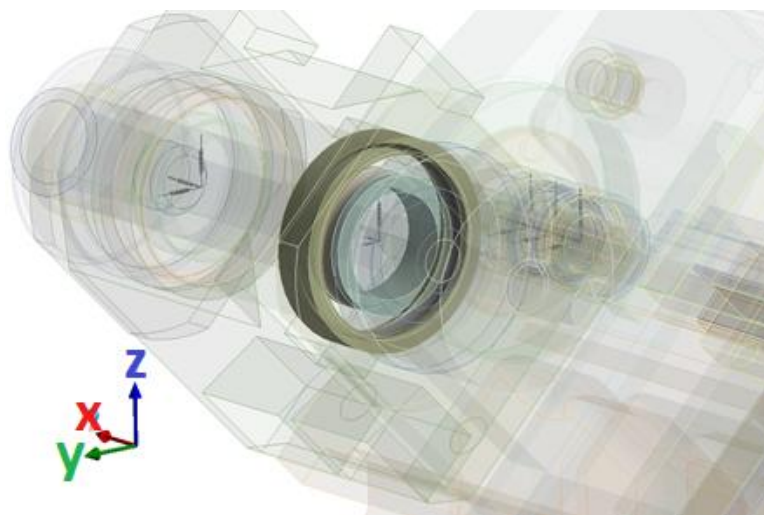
Підшипник передньої бабки токарного верстат
